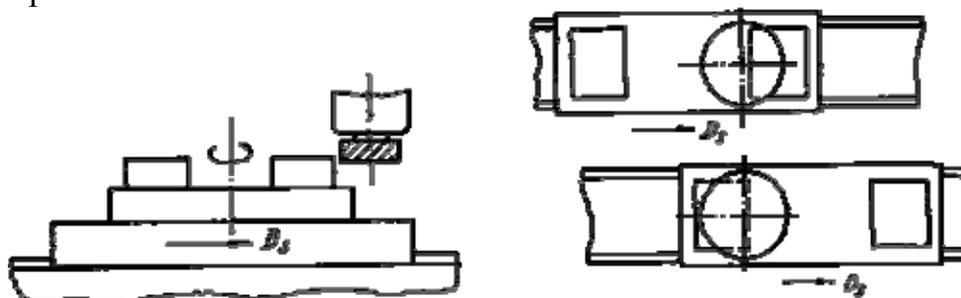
Обработка на двухпозиционном станке (а) и «маятниковая» обработка (б)
